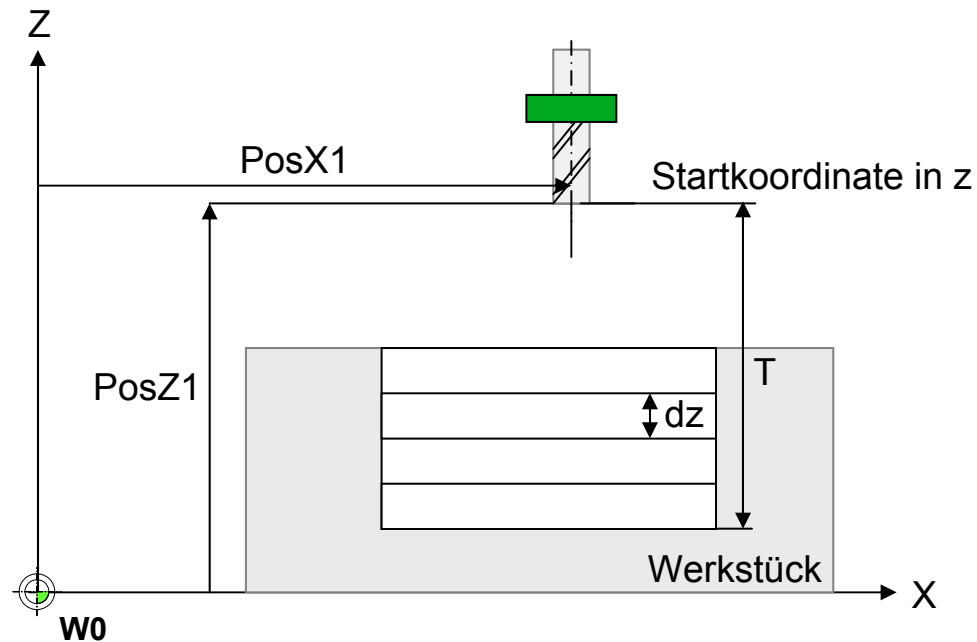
Parameter für die Definition einer rechteckigen Frästasche
